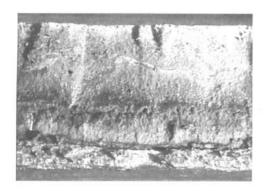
裂纹断口形貌 Fig. 3 Morphology of the crack fracture
